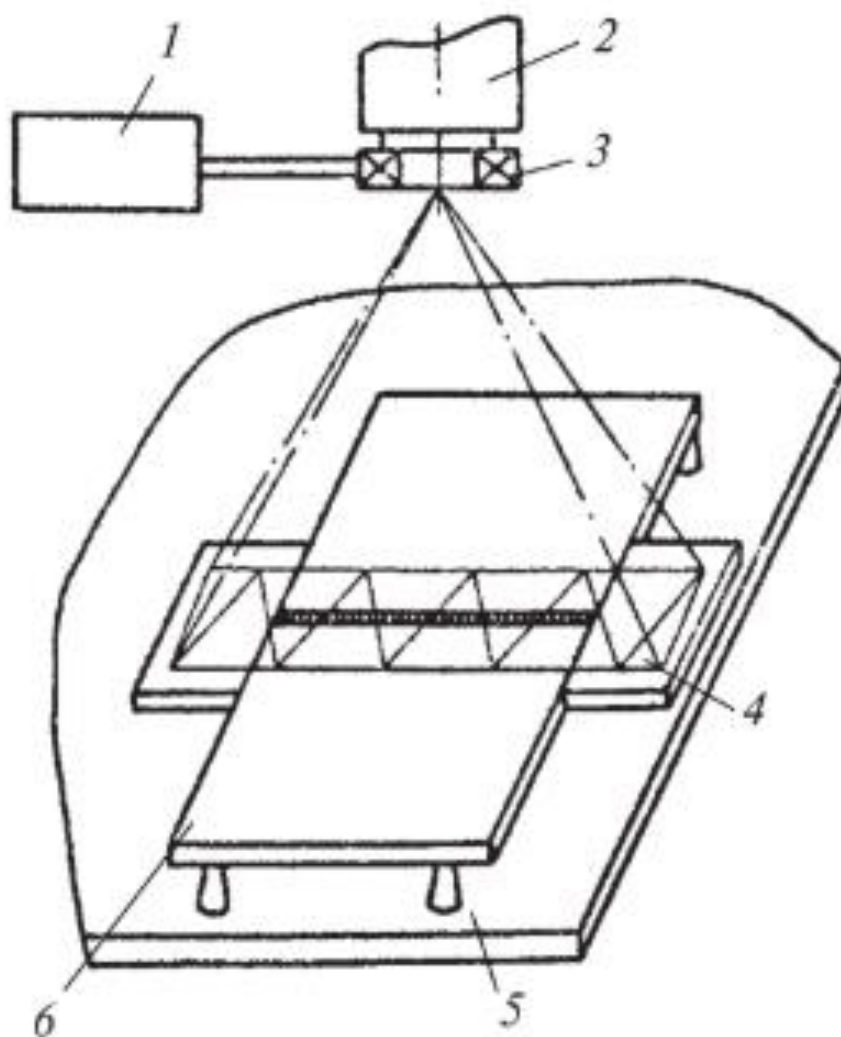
схема проведения локальной термической обработки электронным лучом: 1 – блок управления, 2 – сварочная пушка, 3 – отклоняющие катушки, 4 – зона нагрева, 5 – сборочно-сварочный стол, 6 – обрабатываемая деталь
